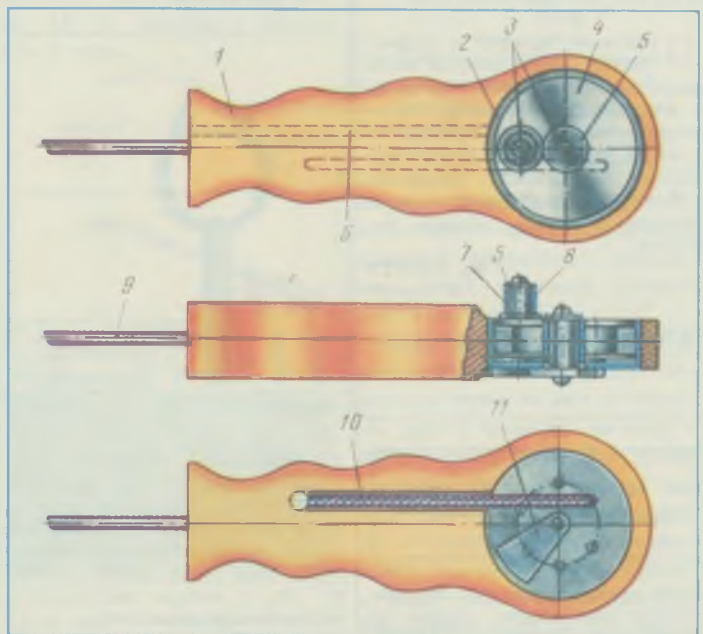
Удочка в сборе: 1 — рукоятка; 2 — корпус катушки; 3 — винт МЗ (3 шт.); 4 — катушка; 5 — пластина; 6 — отверстие для лески; 7 — цилиндр; 8 — ручка; 9 — хлыстик; 10 — тормоз; 11 — сектор.
